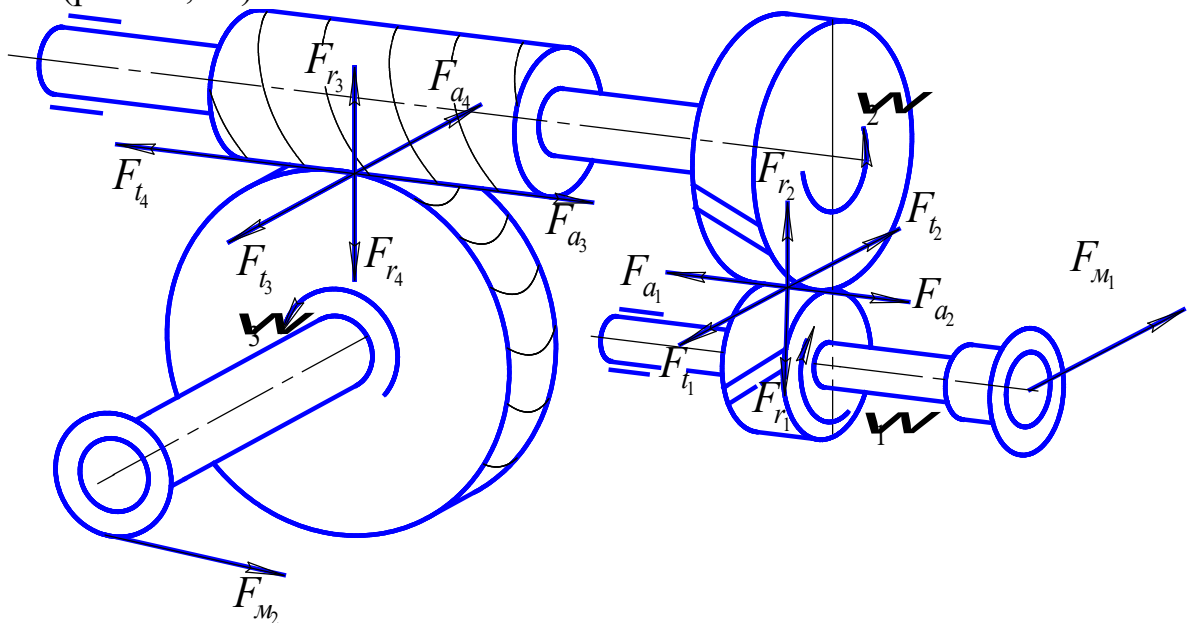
Схема сил зубчато-червячного редуктора в пространстве
